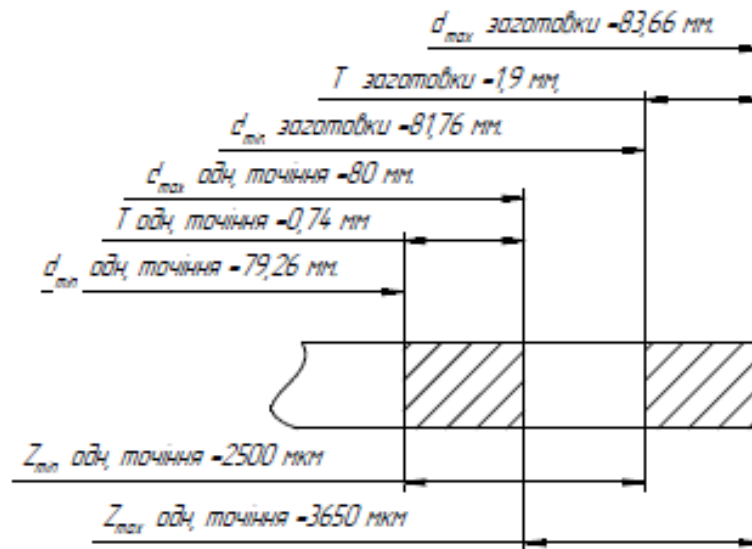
Схема графічного розташування припусків та допусків на обробку поверхні $\varnothing 80h14_{(-0,74)}$
